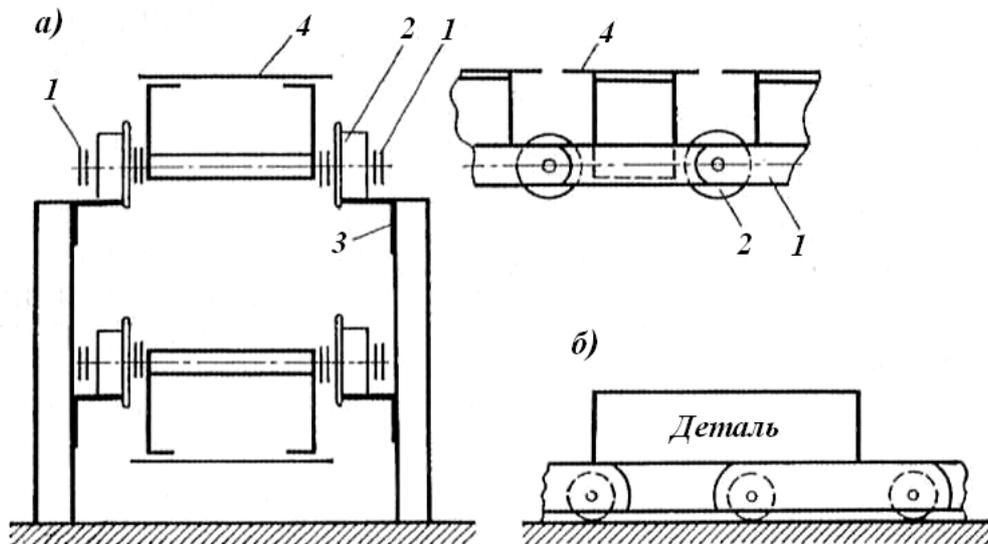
Пластинчатый конвейер: 1 – втулочно-роликовая цепь; 2 – опорные катки; 3 – поддерживающая конструкция; 4 – несущая пластина
